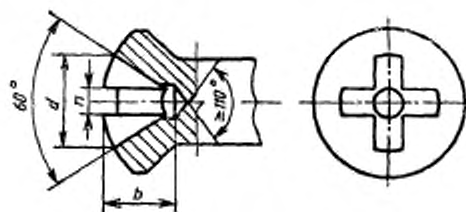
Головка с внутренним крестообразным шлицем
